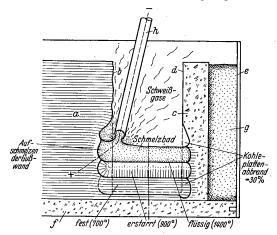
Der Vorgang einer elektrischen Warmschweißung an einer Bruchwand (links) und einer Formkohlewand (rechts).
